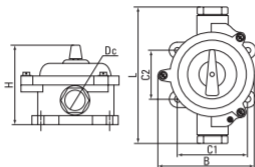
Пакетные выключатели серии ПВ – Исполнение в силуминовом корпусе
